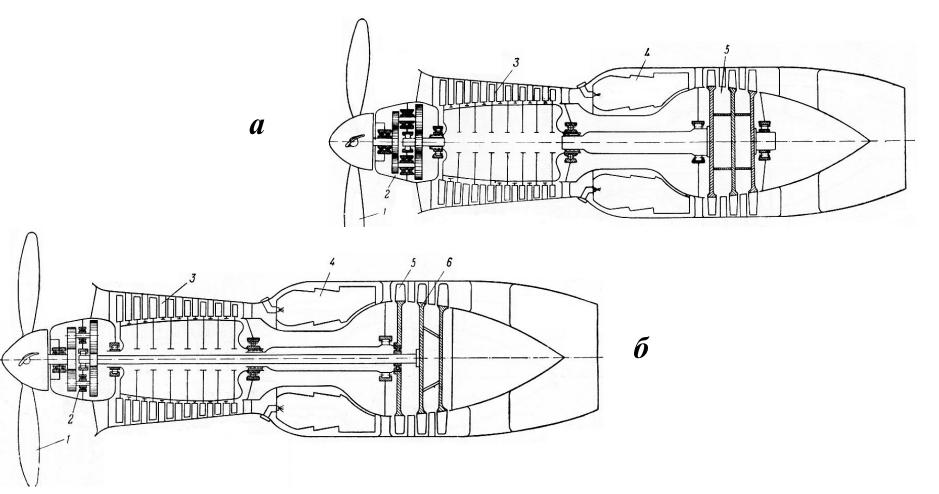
Схемы ТВД. *a* – с общей турбиной, *б* – с раздельными турбинами. 1– воздушный винт; 2– редуктор числа оборотов; 3– компрессор; 4– камера сгорания; 5– турбина; 6– турбина винта.
